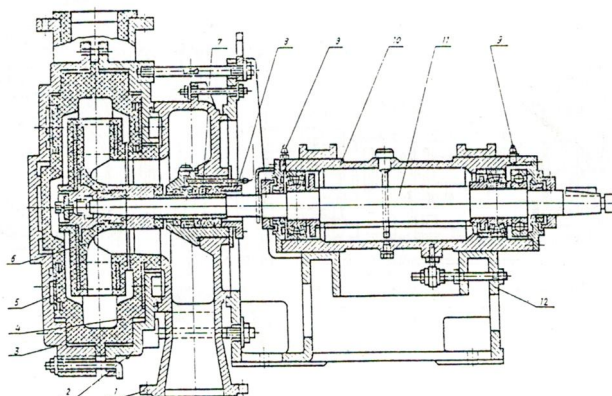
Разрез насоса типа НПБР: 1 — подвод (на рисунке повернут на 90°); 2 — передний корпус; 3 — задний корпус; 4 — передняя футировка отвода; 5 — задняя футировка отвода; 6 — рабочее колесо; 7 — защитная втулка; 8 — узел сальникового уплотнения; 9 — шариковые пресс-масленки; 10 — стакан; 11 — вал; 12 — узел опорной стойки.
